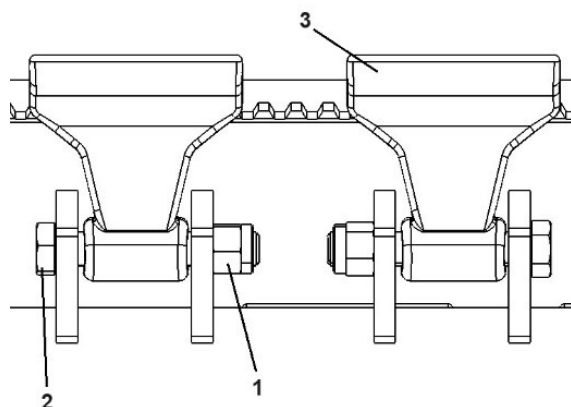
Austausch der Schlegelmesser: 1 – Befestigungsmutter, 2 – Befestigungsschraube, 3 – Schlegelmesser
